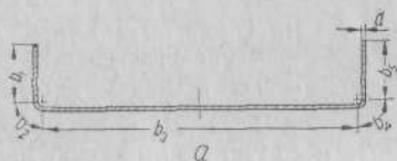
Схемы разбивки профилей на элементы для определения ширины исходной заготовки:
